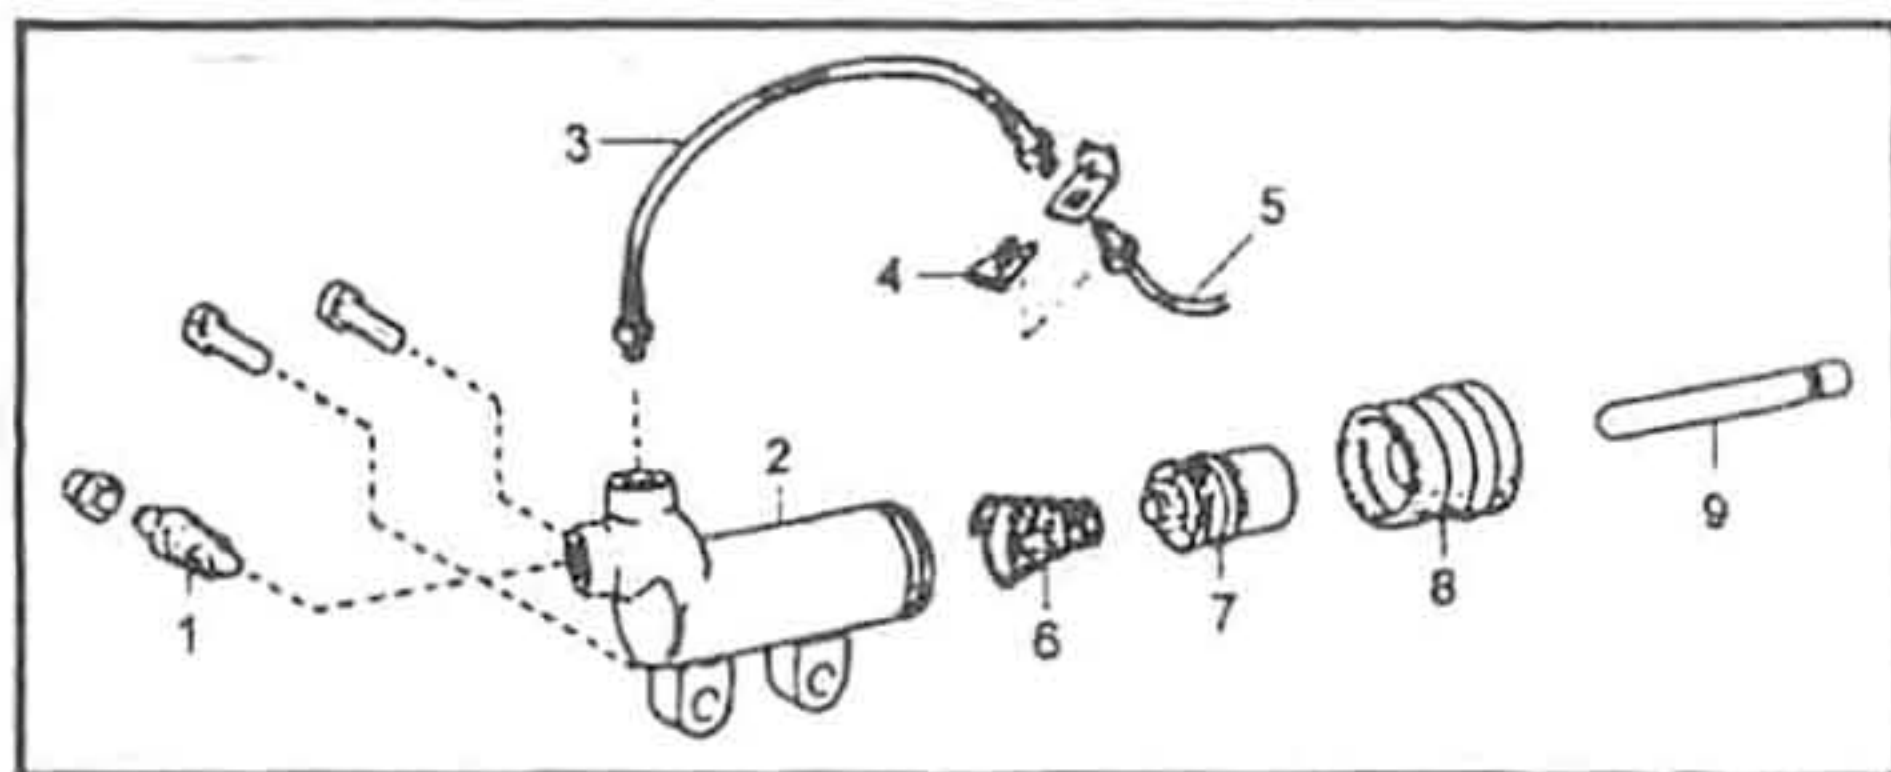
1. Клапан выпуска воздуха. 2. Корпус. 3. Тормозной шланг. 4. Замок. 5. Трубка гидросистемы. 6. Пружина. 7. Поршень. 8. Чехол. 9. Нажимной шток.
